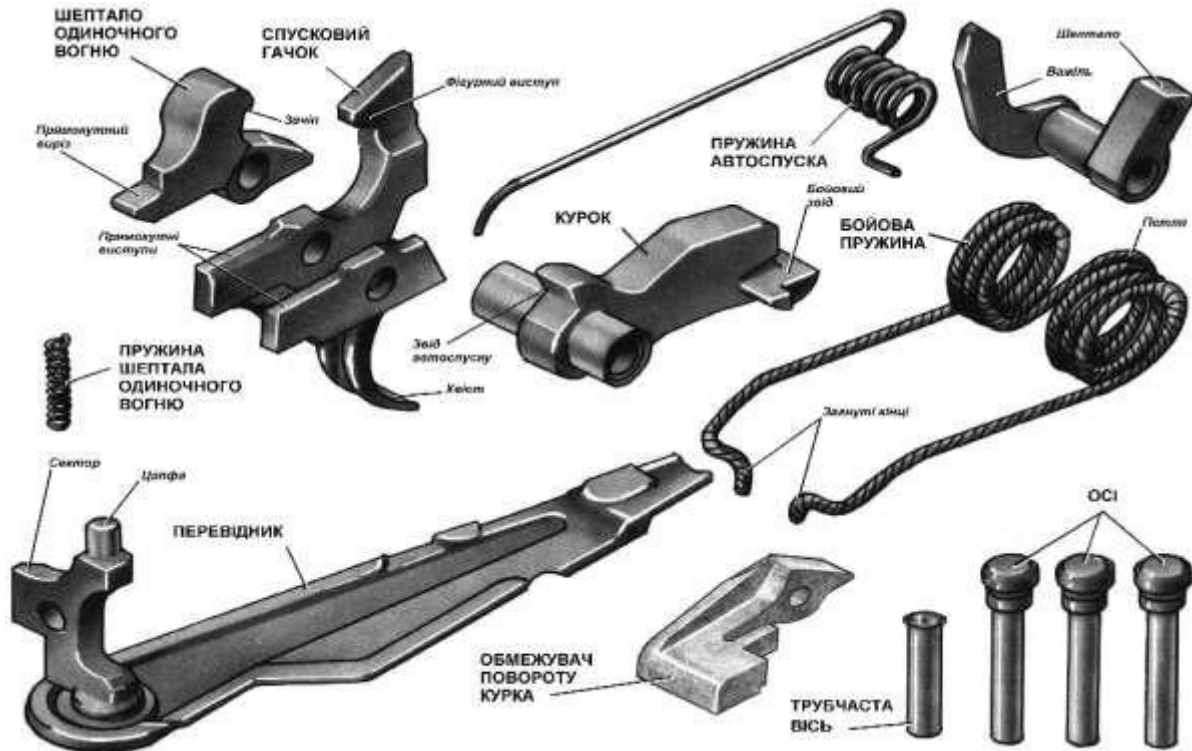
Ударно-спусковий механізм автомата Калашникова
